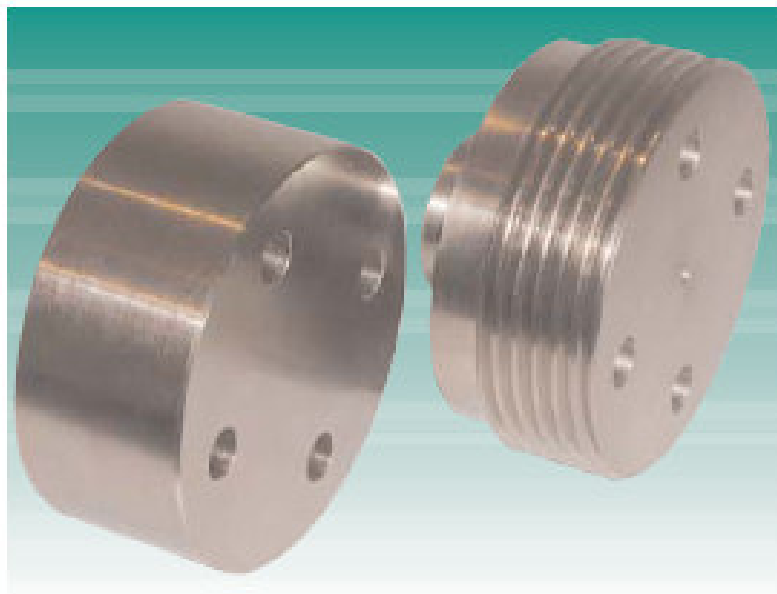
Čelisti se šroubovým systémem upnutí pro zkoušku tahem drátů
